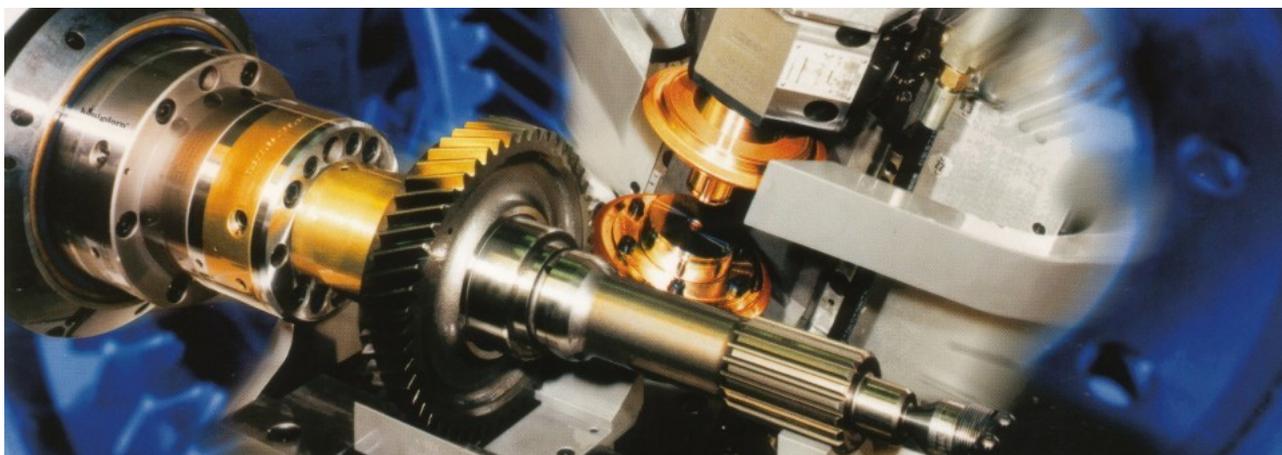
Обработка вал-шестерни на станке с ЧПУ
